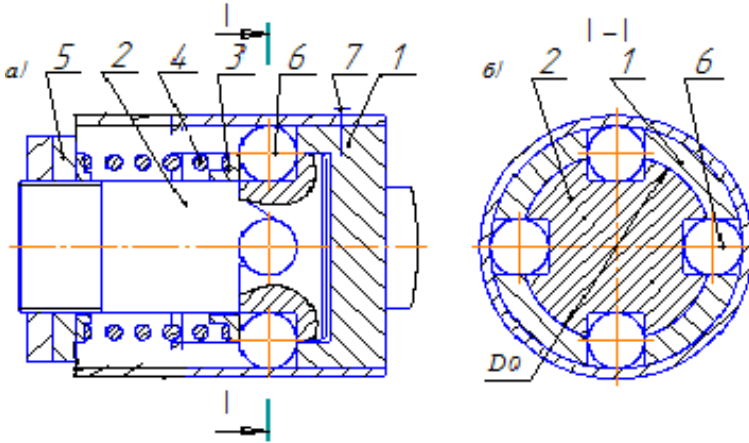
Принципова схема муфти: а) загальний вигляд; б) переріз I-I
